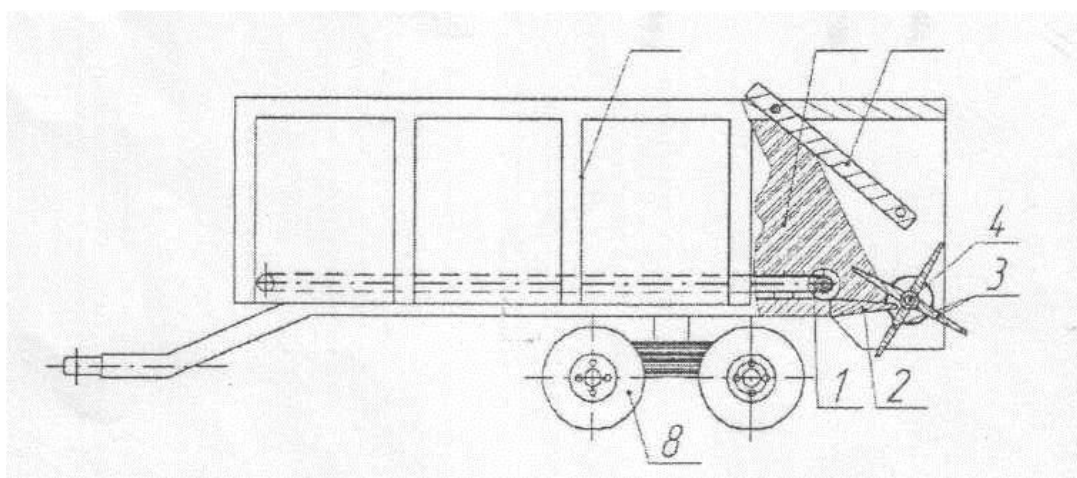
Разбрасыватель-измельчитель подстильного навоза: 1 – цепочно-планчатый транспортер; 2 – противорежущие пластины; 3 – ножи; 4 – вал; 5 – кузов измельчителя; 6 – подстильный навоз; 7 – рама; 8 – колеса; 9 – задний борт
